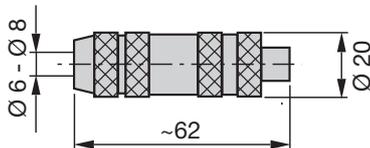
Steckverbinder BKS-S105-00 (Stift) für BUS OUT
